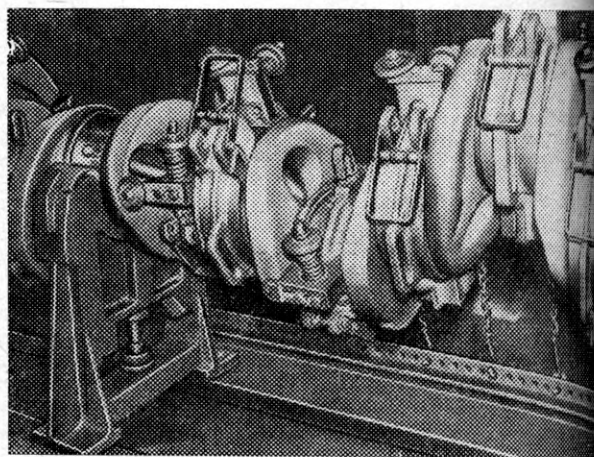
Приспособление для обработки шеек коленчатого вала дизеля с помощью шлифовальной шкурки перед полировкой
